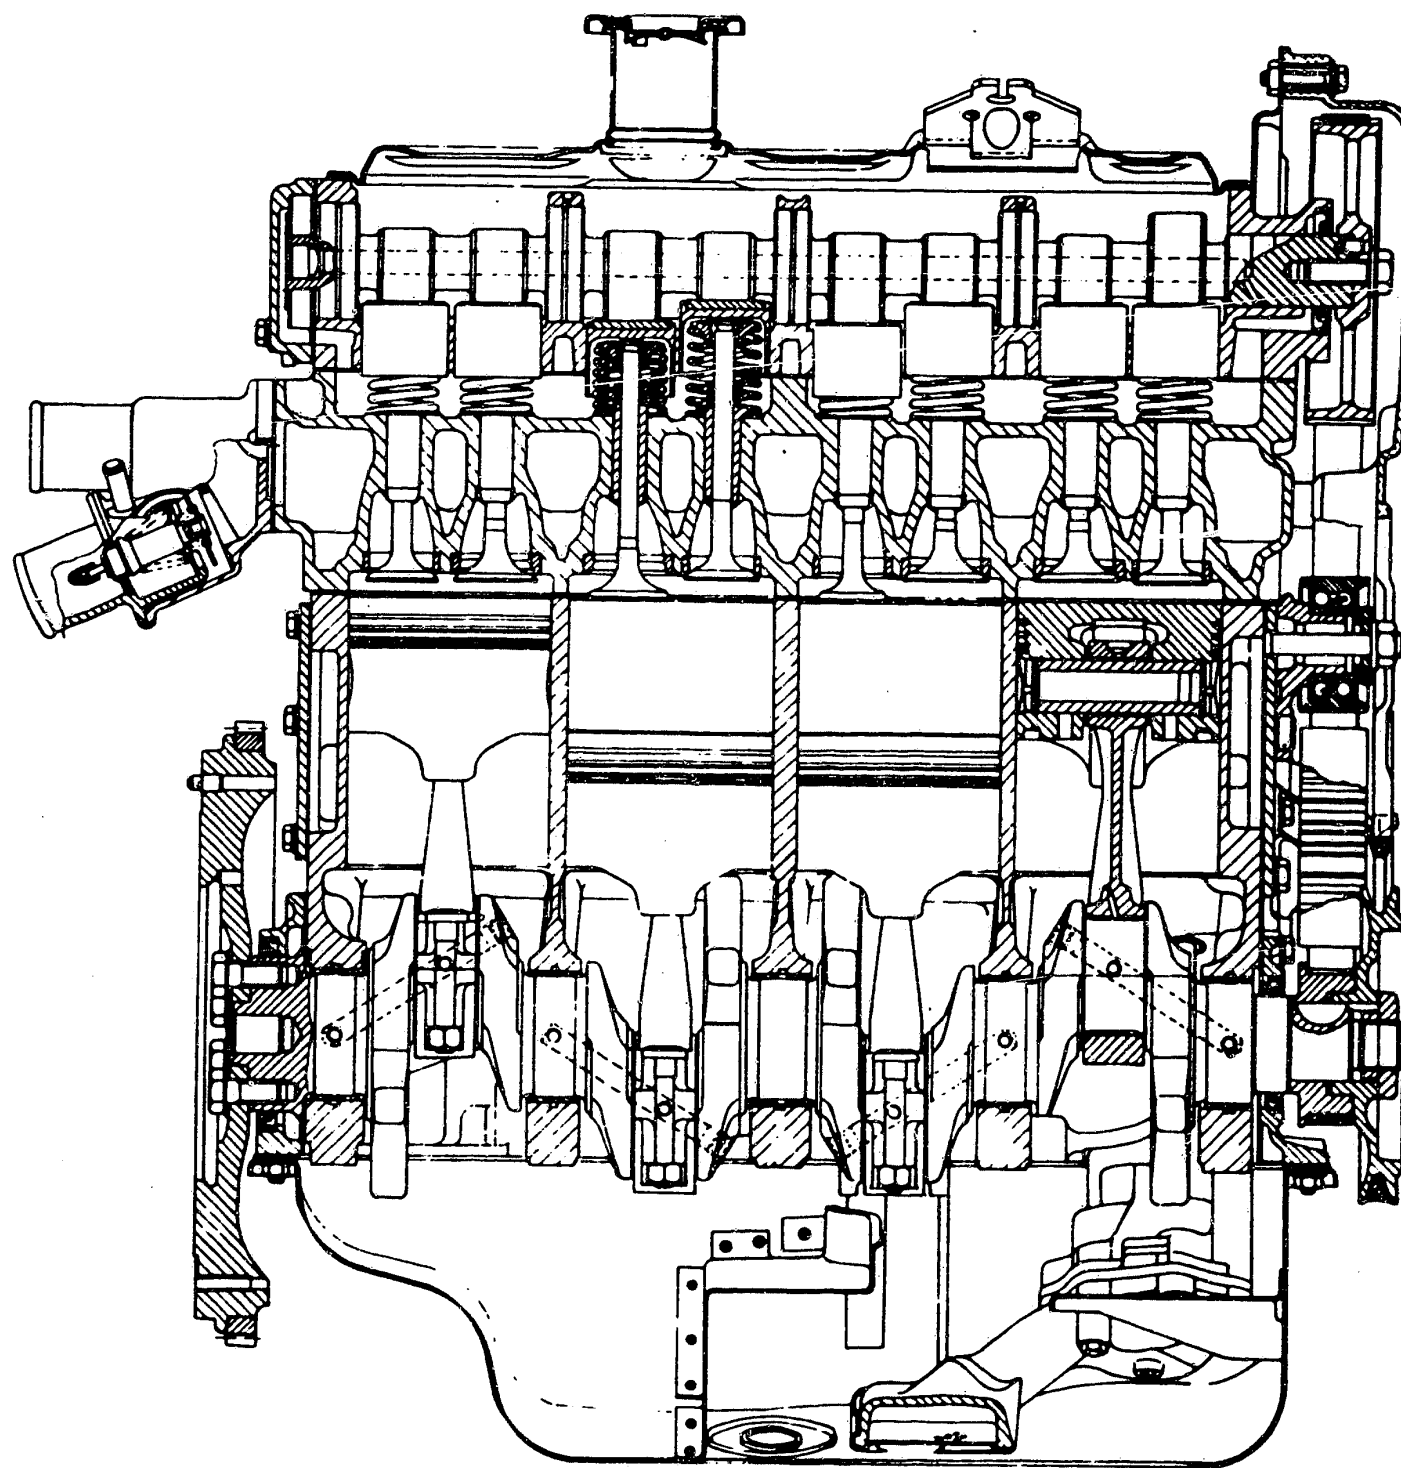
Längsschnitt durch den OHC-Motor mit 1116 oder 1301 cm³ Hubraum.
